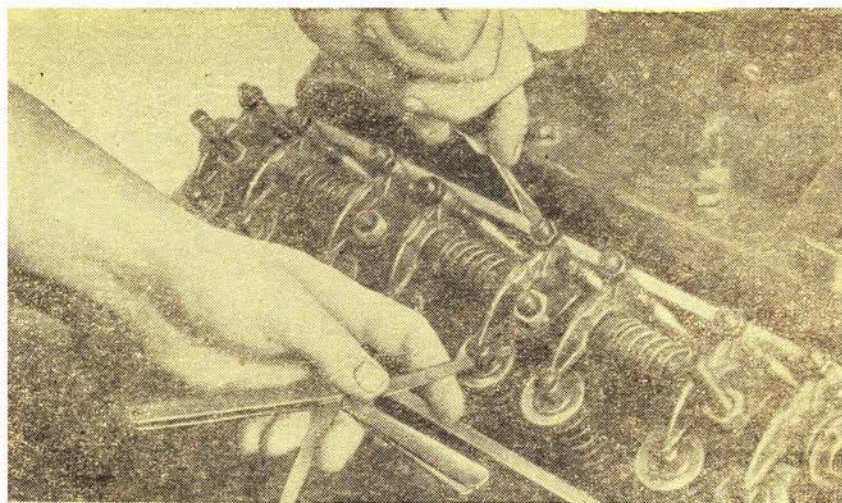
Регулировка зазоров между коромыслами и клапанами.
